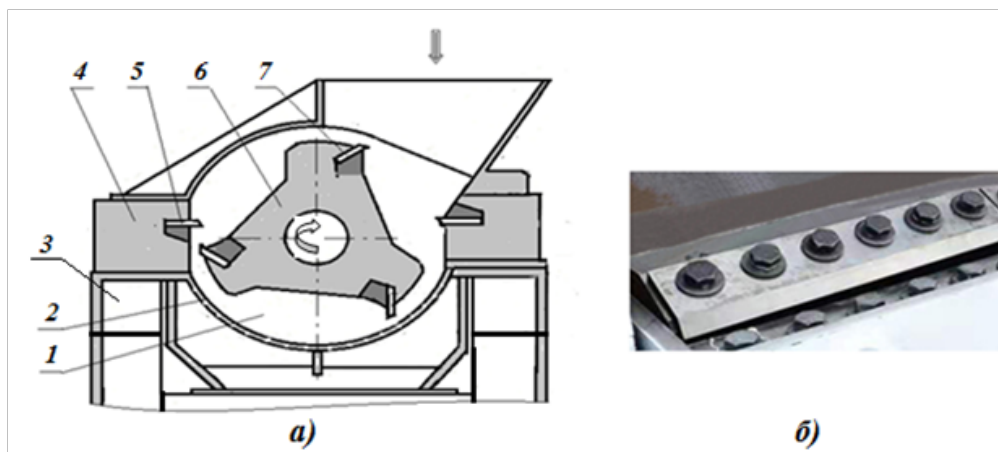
Схема роторного измельчителя пластиковых отходов (а), крепление ножей к ротору (б):
